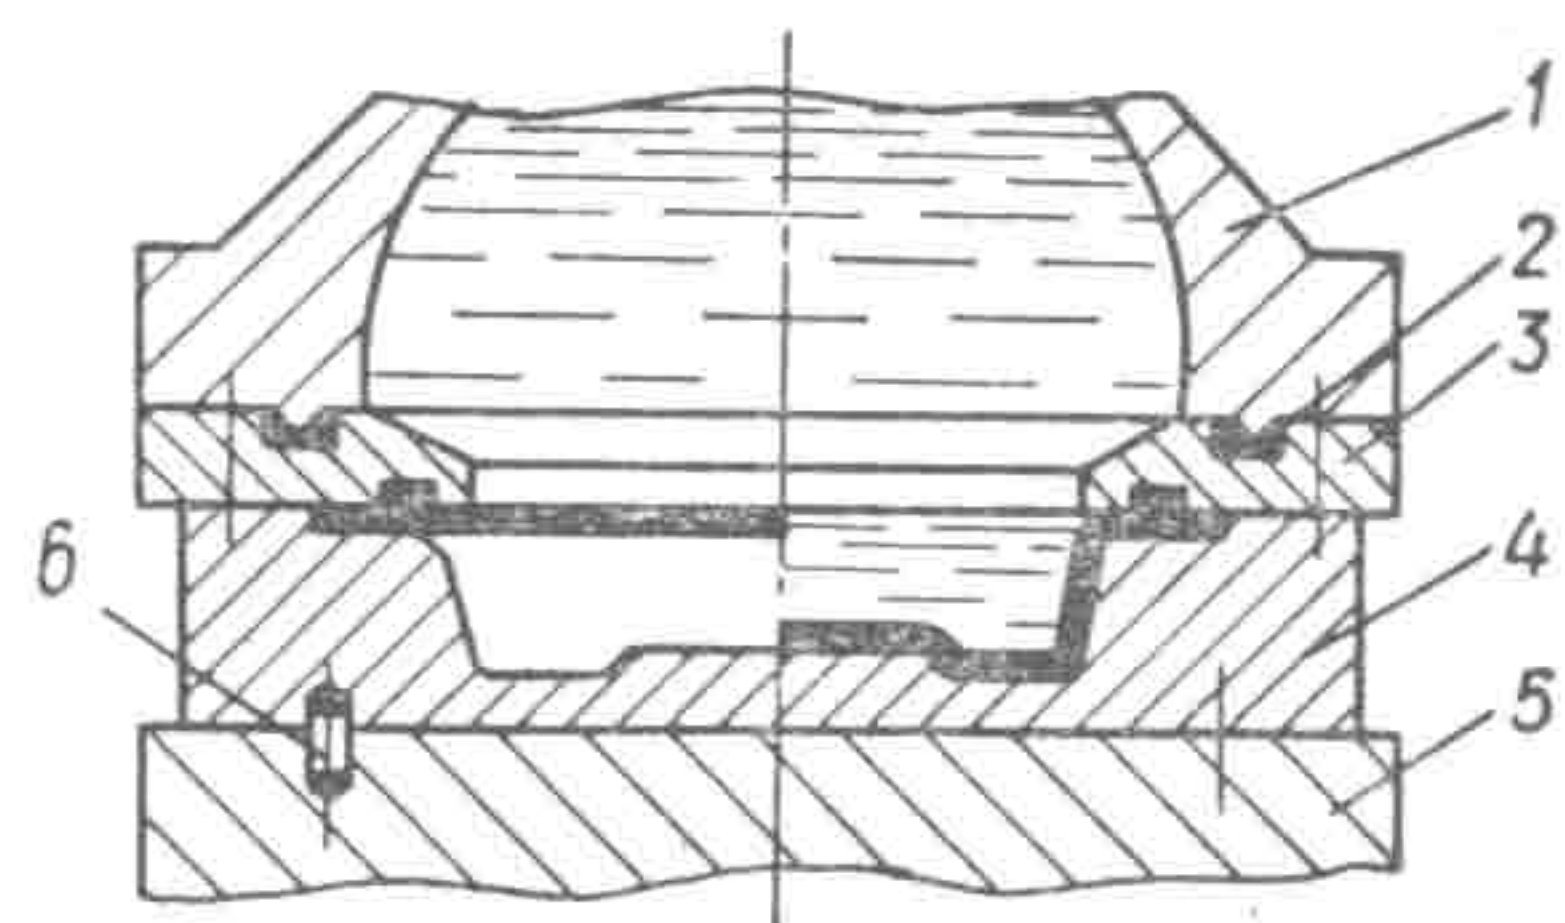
Оснастка для вытяжки крупногабаритных деталей:
